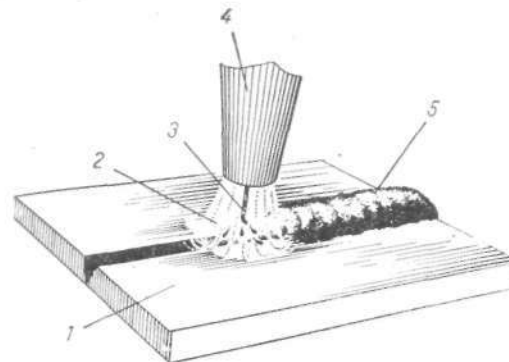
Схема процесса сварки плавящимся электродом в защитных газах.
